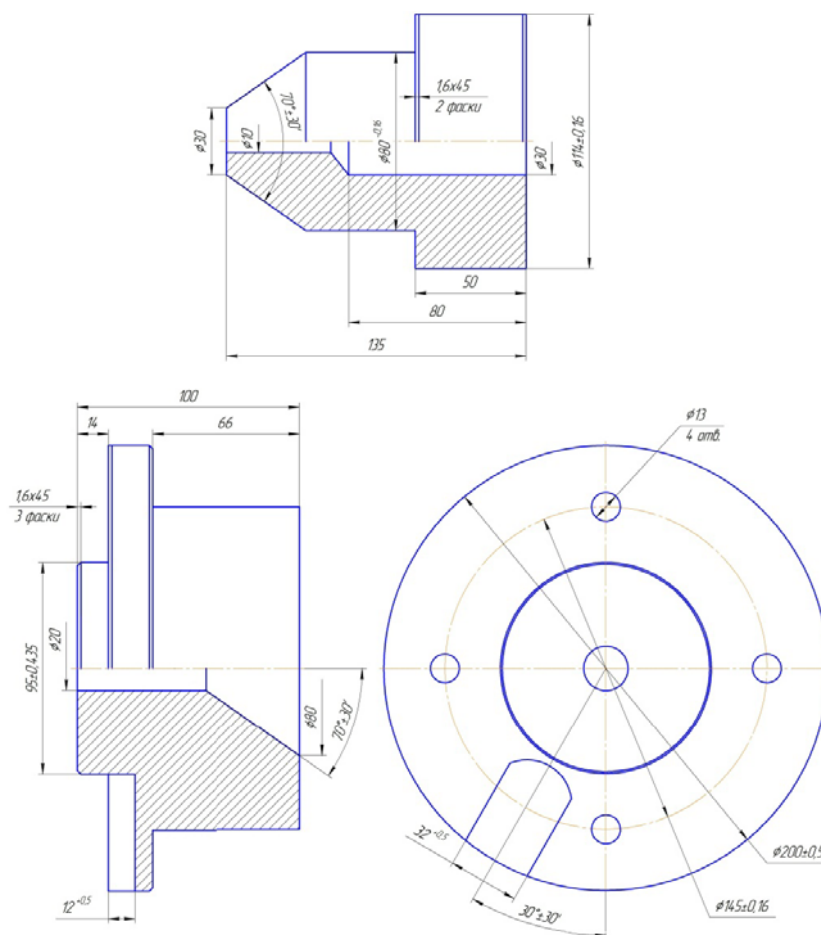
Эскиз имитаторов патрубка и корпуса патрубкового узла
